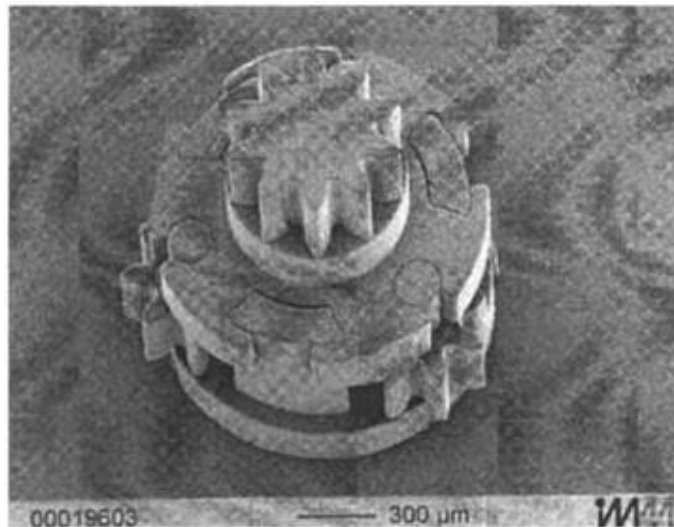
Un microengranaje fabricado por técnica de LIGA.
